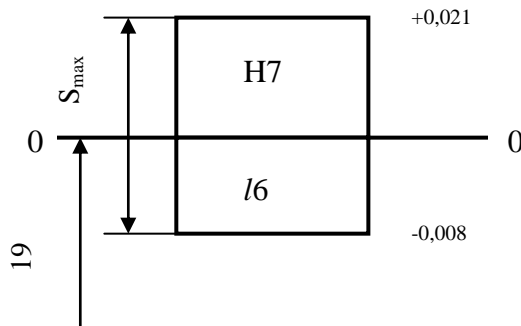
Схема посадки наружного кольца подшипника качения
